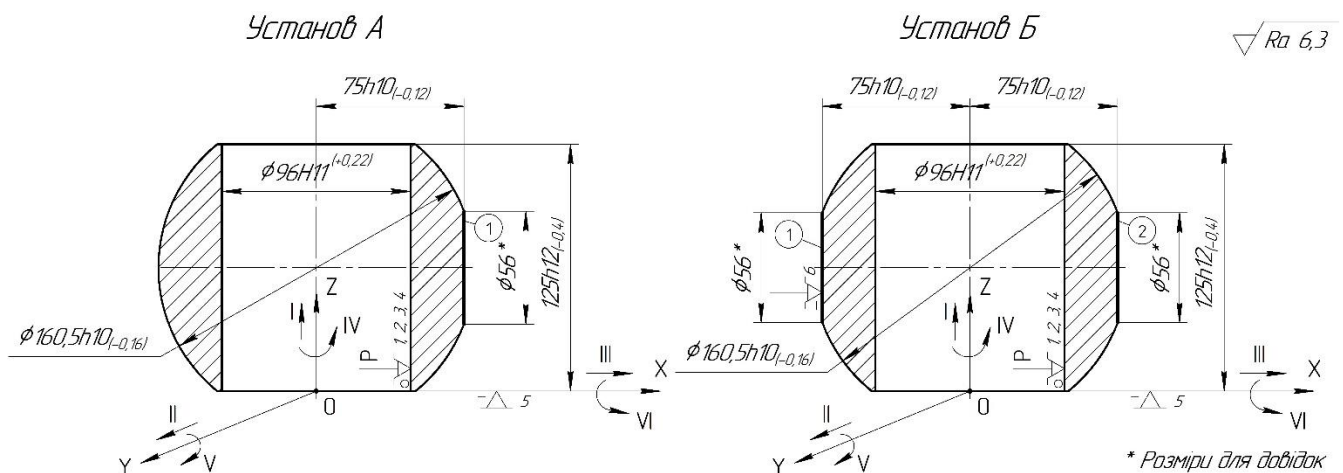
Схеми базування заготовки на установах А і Б операції 035
